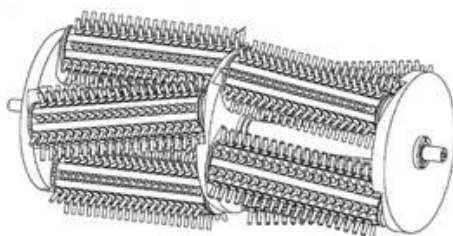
Общий вид фрезерного агрегата с карданным подвесом – барабан с установленными сателлитами
